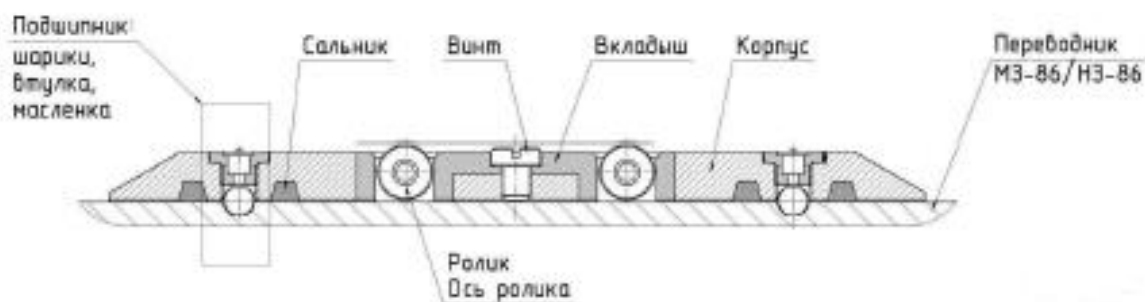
Центратор роликовый вращающийся ЦР-136
